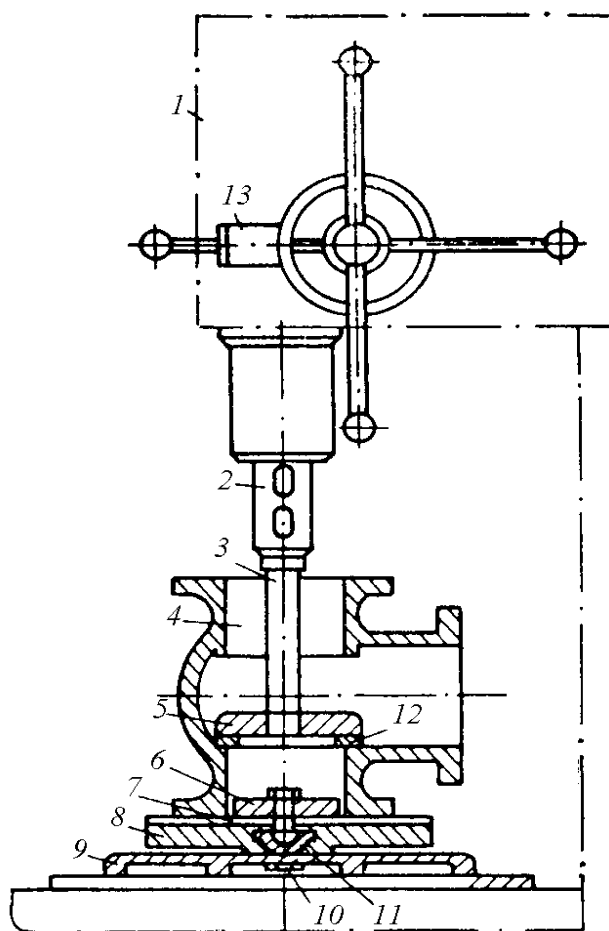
Приспособление для притирки уплотнительной поверхности корпуса задвижки на сверлильном станке:
